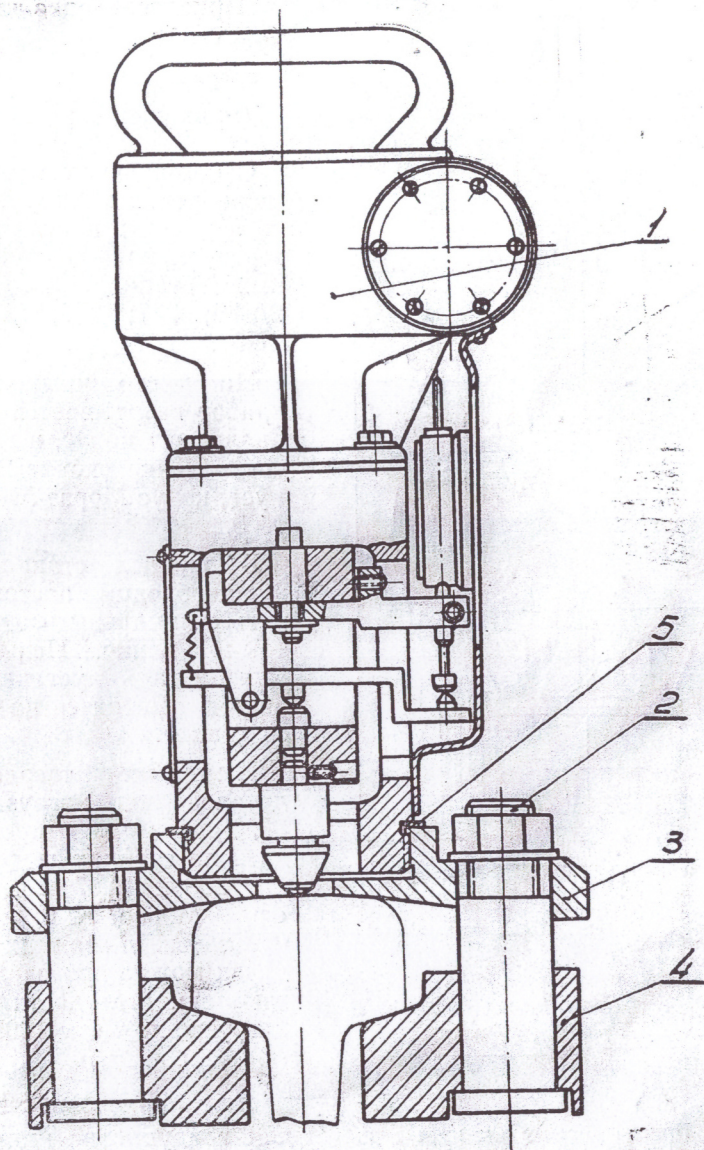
Приспособление для крепления прибора к головкам рельсов:
